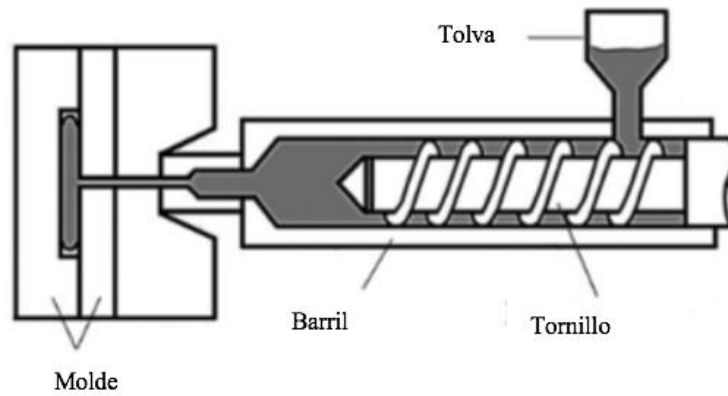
Vista general de componentes fundamentales que componen el moldeo por inyección de plástico (Zheng et al., 2011).
